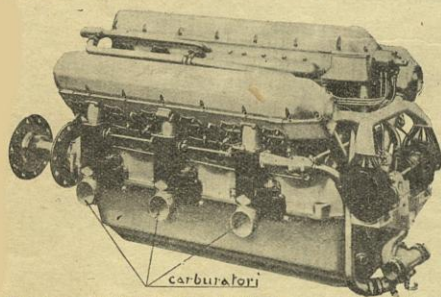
Installazione dei carburatori su un motore raffreddato ad acqua.
